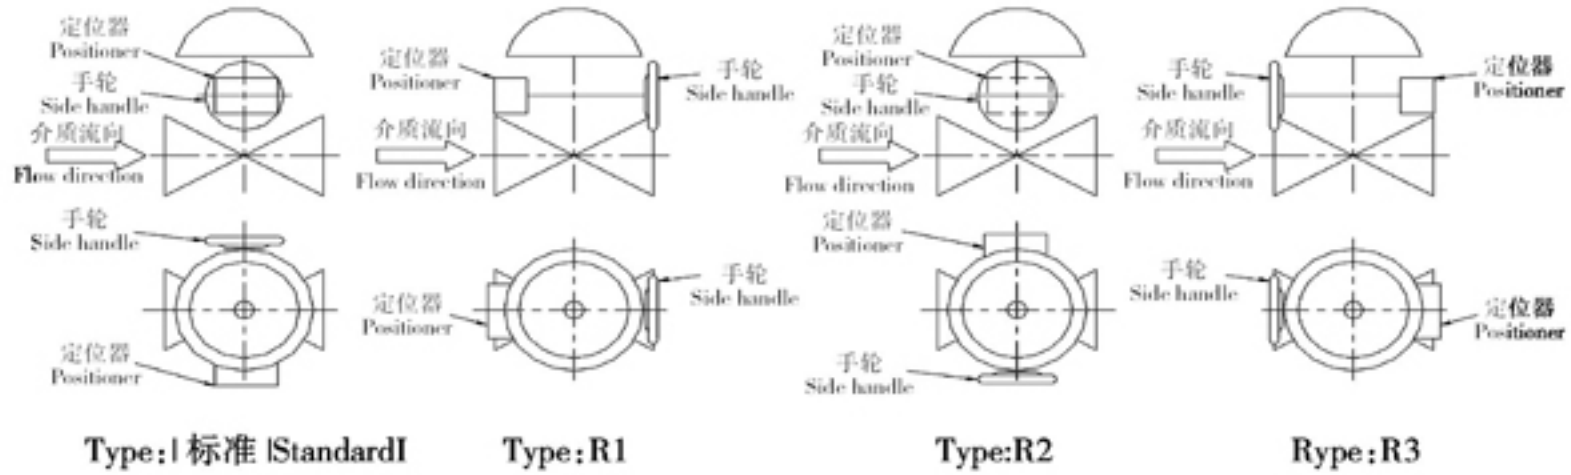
配 MF5 执行机构的安装位置 Fig.5-2. Mounting forms with MF5 actuator
